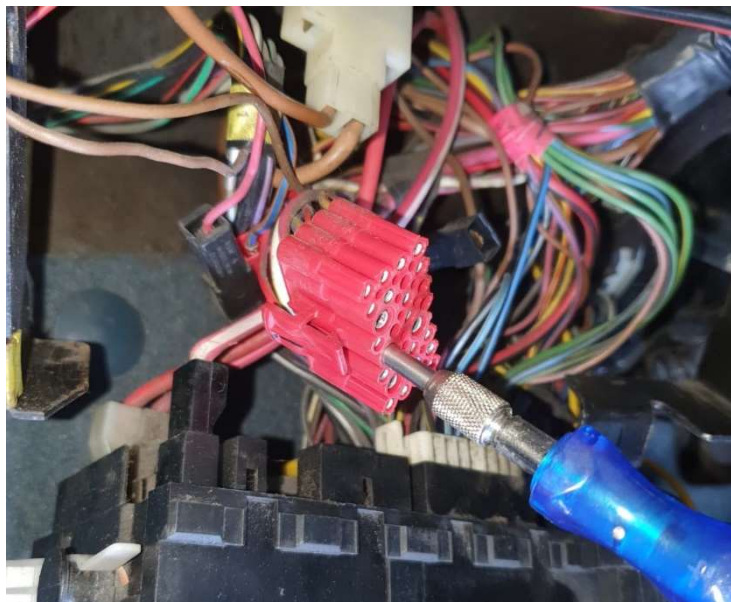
Auspinnen des Rundsteckkontakts B22 am roten Stecker
